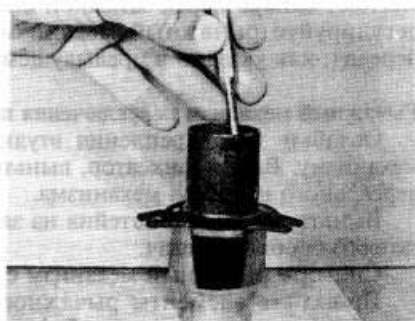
Извлечение сальника из направляющей втулки подшипника выключения сцепления
